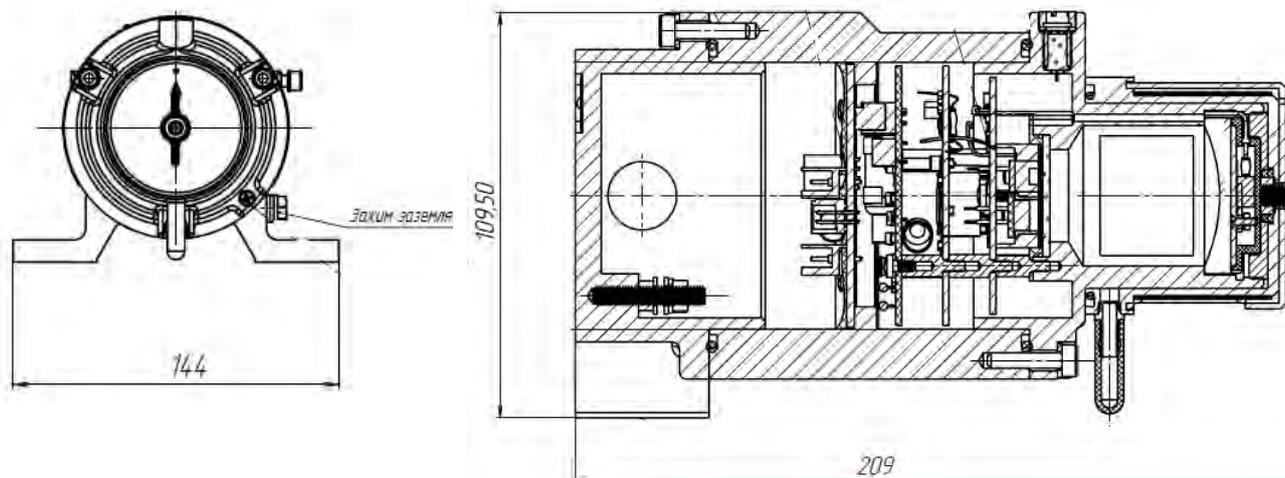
Габаритные размеры ИГМ-14 (корпус тип 5)
